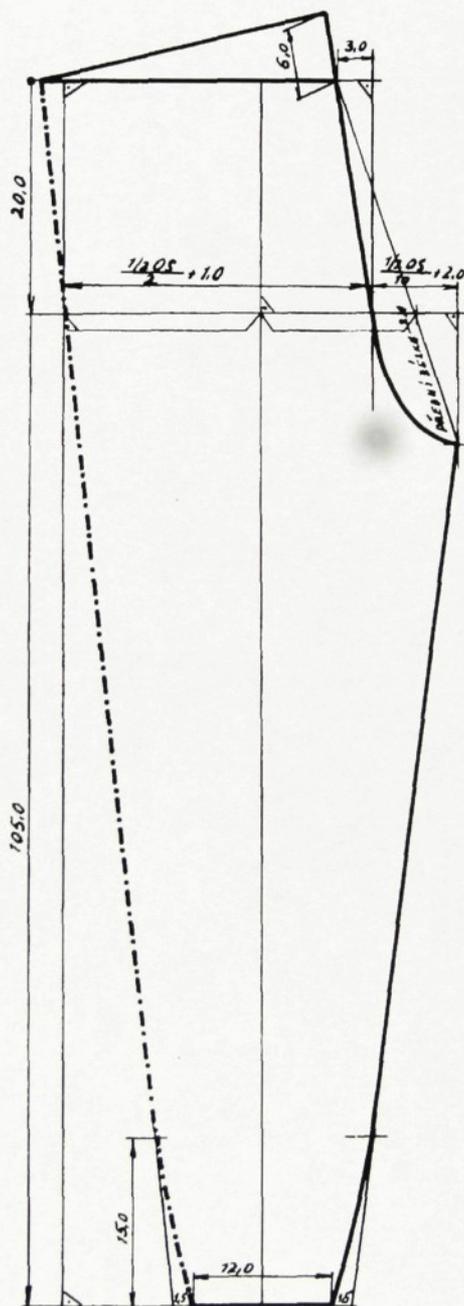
konstrukce teplákových šponovek podle slovenské konstrukce střihů.
